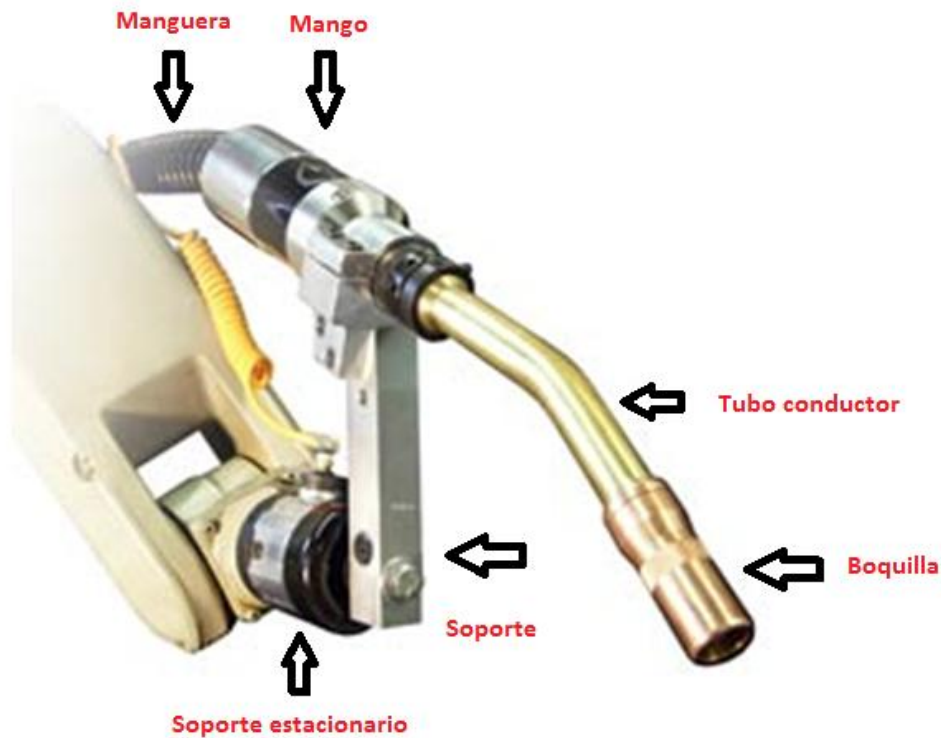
Componentes de una pistola de soldadura montada en robot
